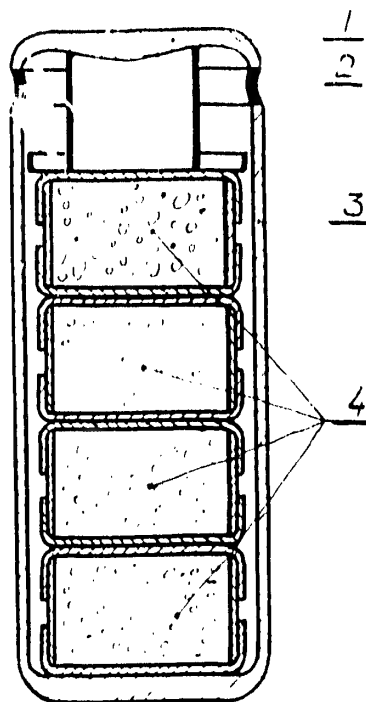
Разрез герметичного блочка. (1-крышка, 2-место сварки крышки с корпусом, 3-корпус, 4-пеналы с облучаемым материалом)
